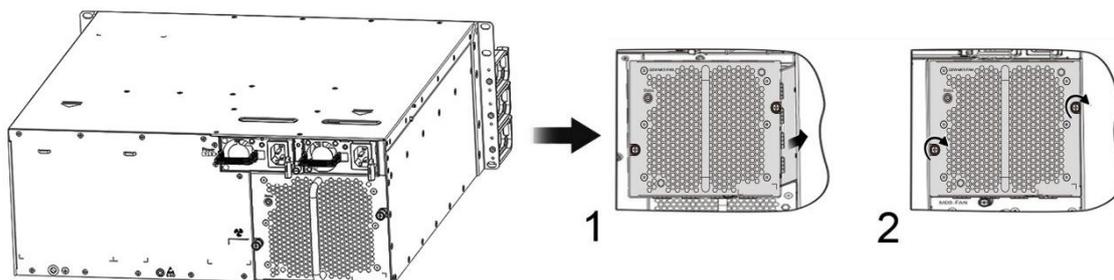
Установка корзины для вентиляторов QSW-M05-FAN
